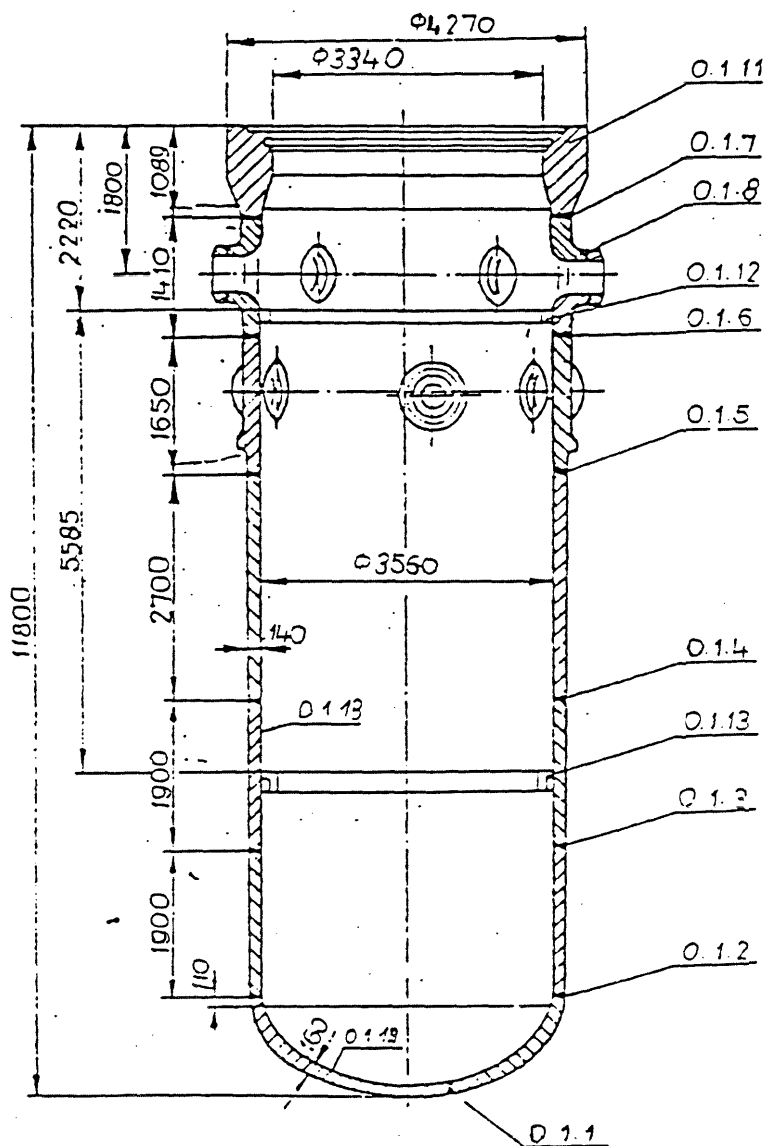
Корпус реактора ВВЭР-440;В-230
